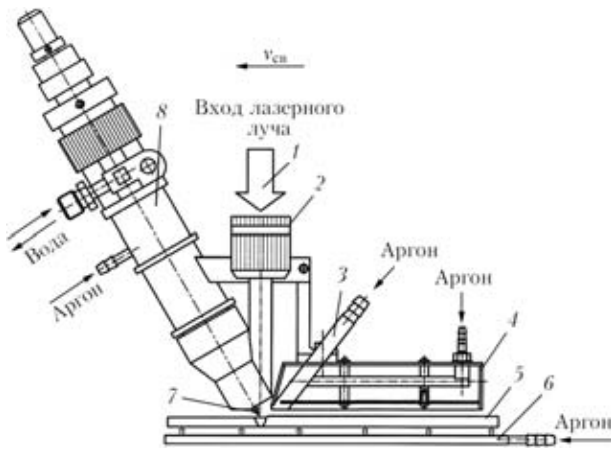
Схема гибридного лазерно-дугового процесса сварки: 1 — лазерный луч; 2 — устройство для фокусировки; 3 — приспособление для дополнительной подачи защитного газа; 4 — приспособление для защиты зоны сварки и остывающего металла шва и ЗТВ; 5 — свариваемый образец; 6 — приспособление для защиты обратной стороны соединения; 7 — вольфрамовый электрод; 8 — сварочная горелка для сварки ТИГ титана
